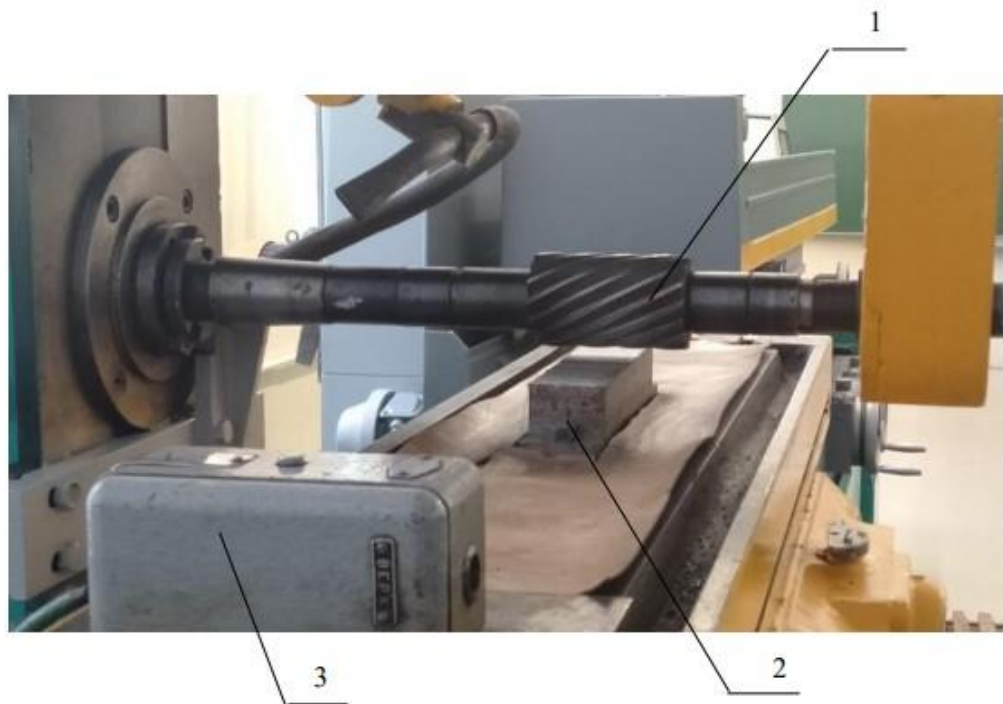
Фото установки детали и инструмента на станке: 1 – фреза; 2 – заготовка; 3 – сейсмодатчик
